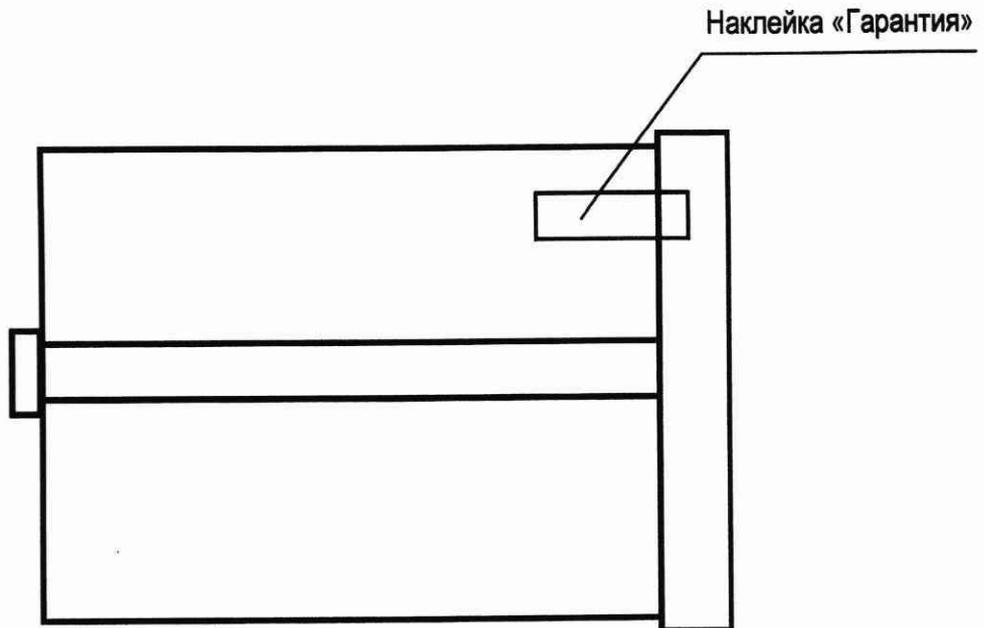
Боковая поверхность корпус Р, Е
